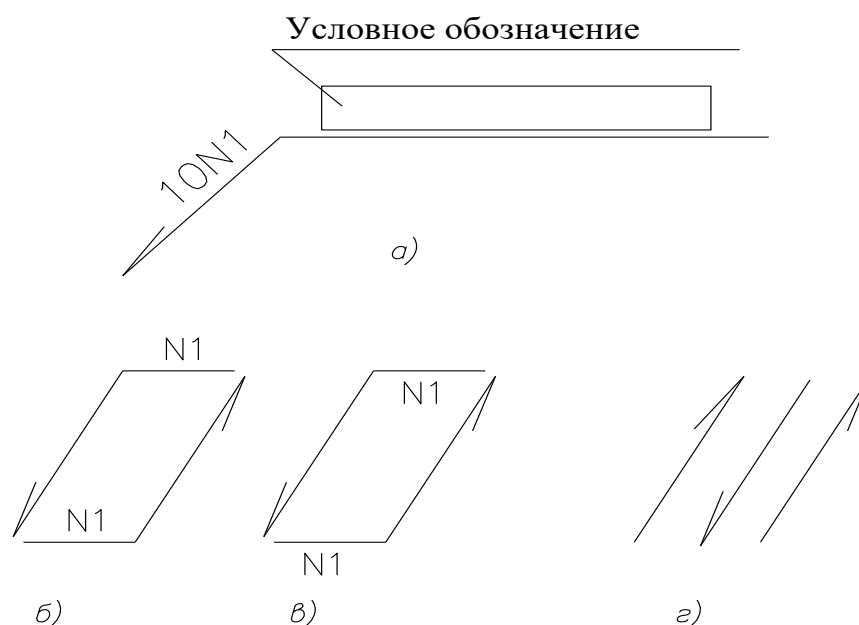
Упрощения в обозначении швов сварных соединений
